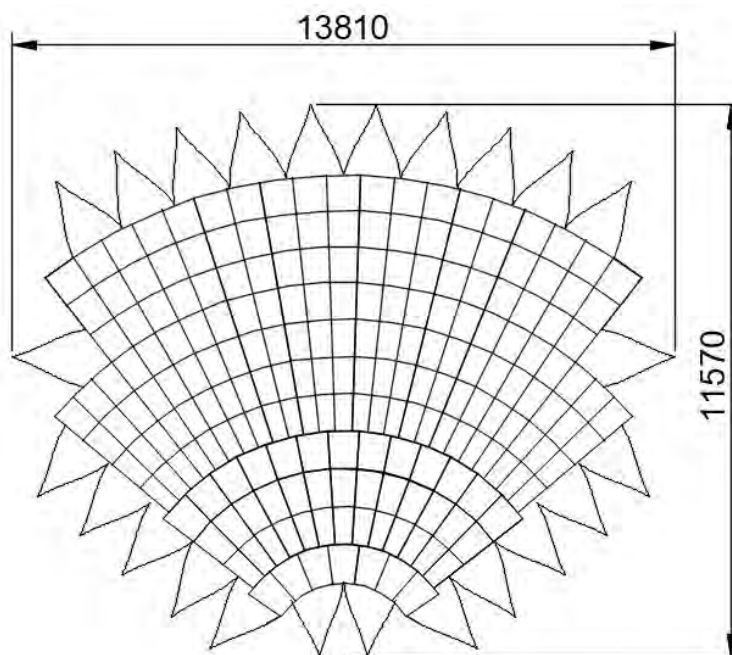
Внешний вид зеркала коллиматора МАРК-12
